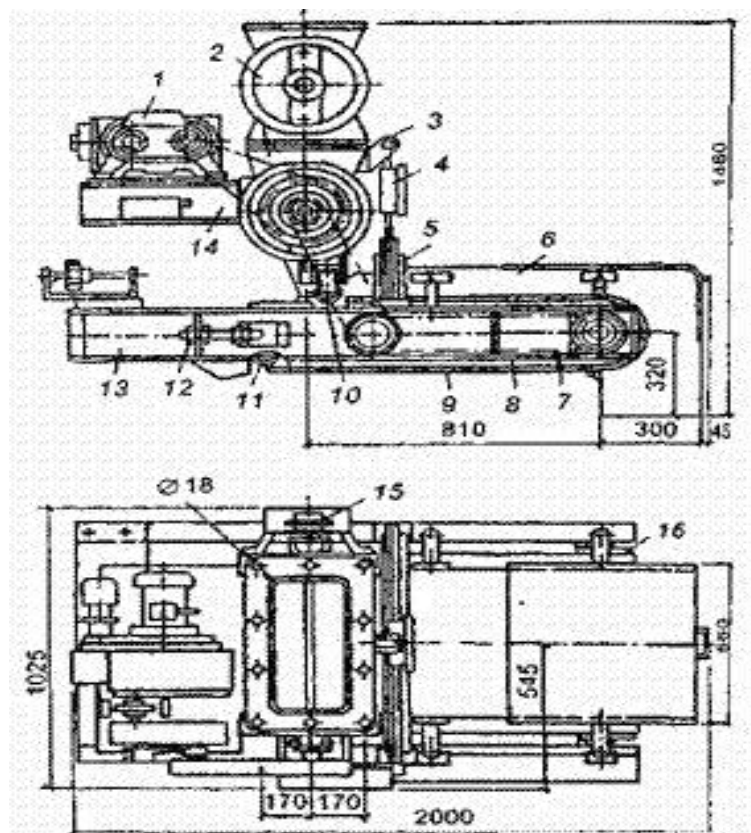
Дозатор СБ-71 А. 1 - привід дозатора; 2 - живильник двухбарабанный; 3 - кронштейн; 4 - датчик зусилля; 5 - кронштейн на щоках конвеєра; 6 - навіс; 7 - ланцюгова передача; 8 - щока; 9 - стрічка; 10 - опори шарнірні; 11 - натяжна барабан; 12 - натяжна гвинт; 13 - ваговий конвеєр; 14 - двоступенева ланцюгова передача; 15 - ланцюгова передача, 16 - барабан привідний
